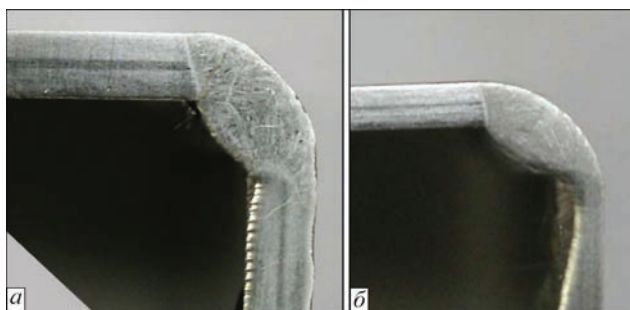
Макроструктура углового сварного соединения из нержавеющей стали AISi 304 толщиной 1,2 мм (а) и AISi 201 толщиной 0,8 мм (б)
